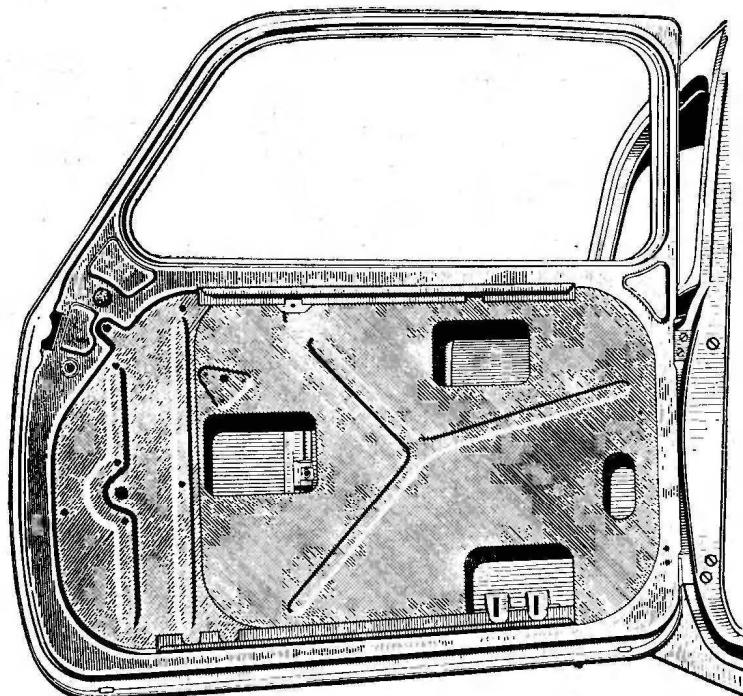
Tür ohne Beschläge, mit Grundanstrich
